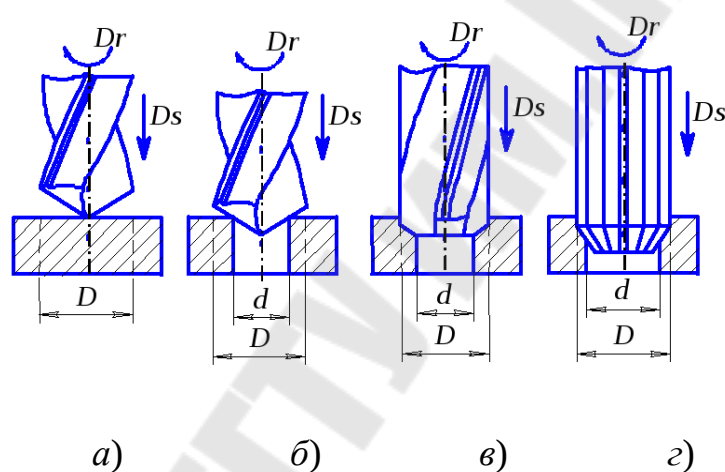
Осевая обработка: а – сверление; б – рассверливание; в – зенкерование; г - развертывание
